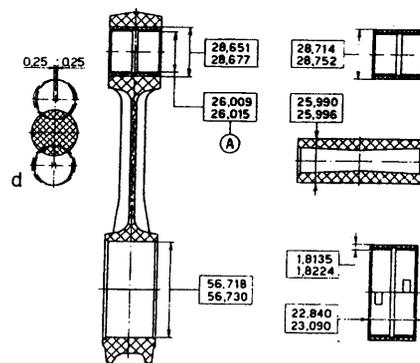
Dimensions normales des bielles, des demi-coussinets, des bagues et des axes.
